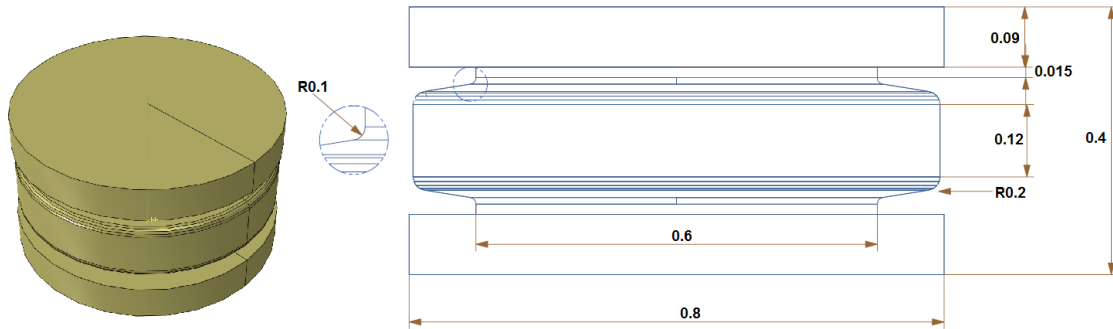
Geometría del rodillo 4, dimensiones en [m].
